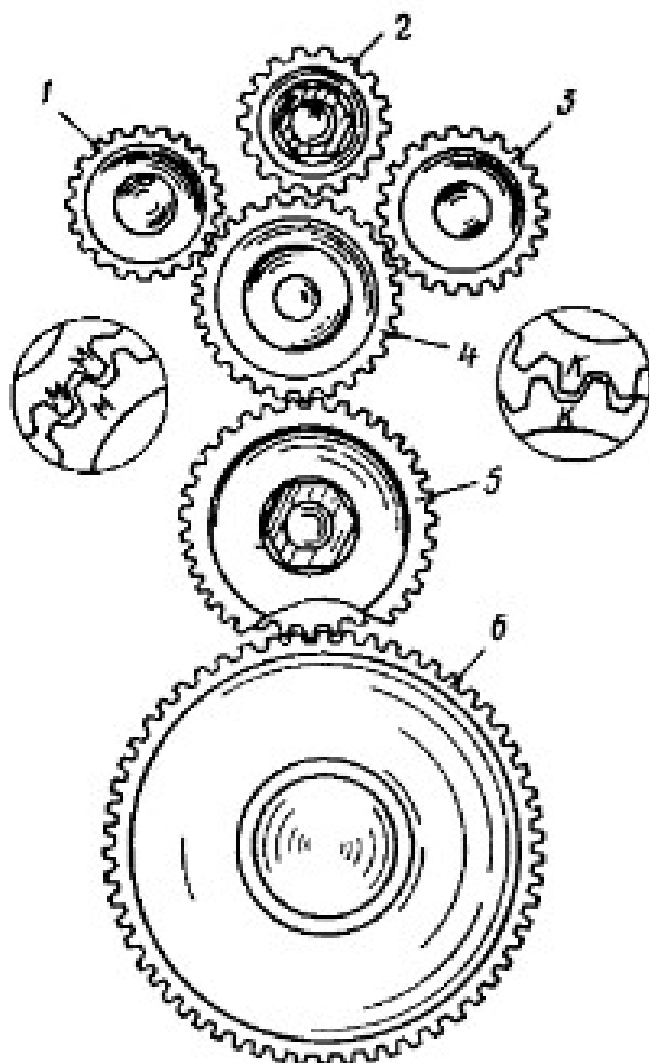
Шестерни распределения пускового двигателя и привода редуктора:
